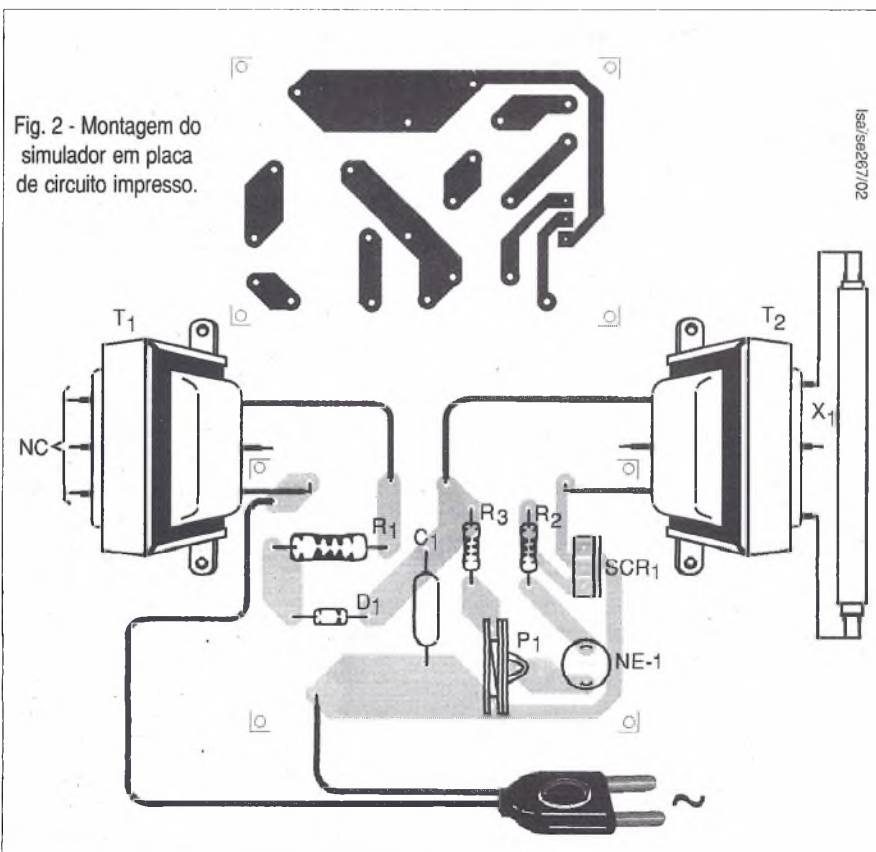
Montagem do simulador em placa de circuito impresso.
